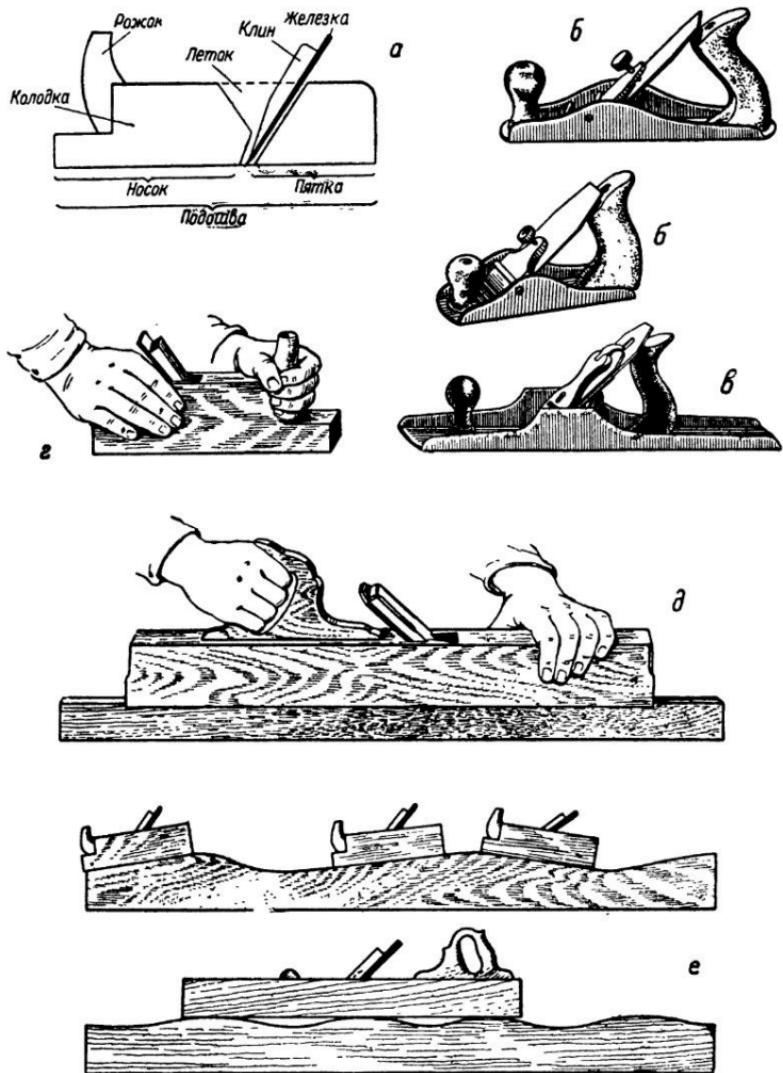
Рубанки: а — схема рубанка; б — металлические рубанки; в — металлический фуганок; г — как держать рубанок; д — как держать фуганок; е — строжка длинной доски рубанком и фуганком.
